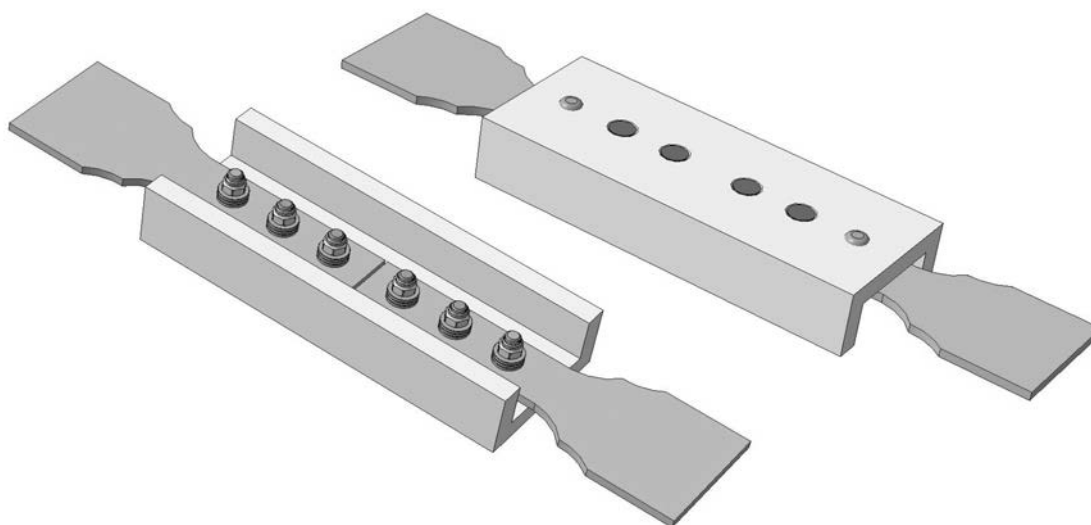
Трехмерная модель образца односрезного болтового соединения с осевым и радиальным натягами для проведения усталостных испытаний
